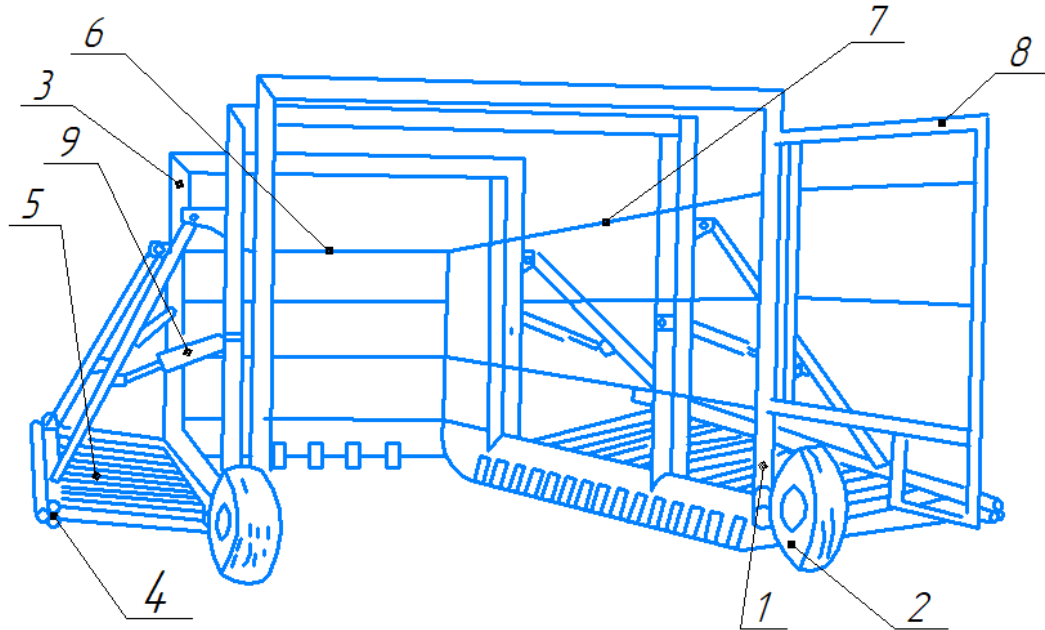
Принципова схема копицево́за: 1 – рама; 2 – задні колеса; 3 – поворотні важелі; 4 – балки вильчастих захватів; 5 – пальці; 6 – передня стінка; 7 – бокові стінки; 8 – задня стінка; 9 – гідроциліндри.
